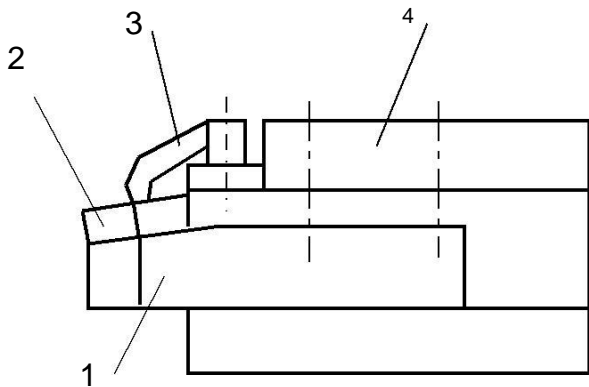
Схема закрепления многогранной режущей пластинки на макете:
